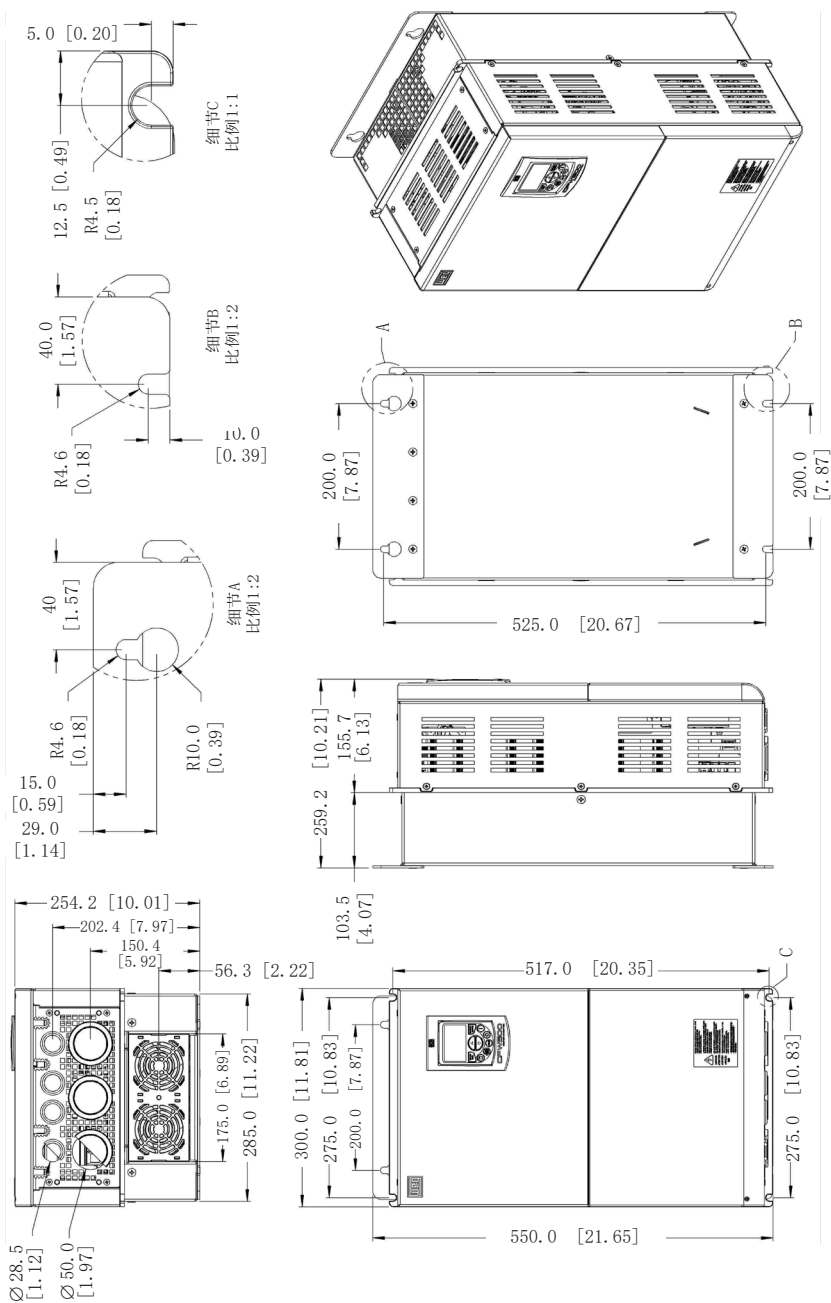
变频器尺寸 - 帧尺寸C - mm [in]
